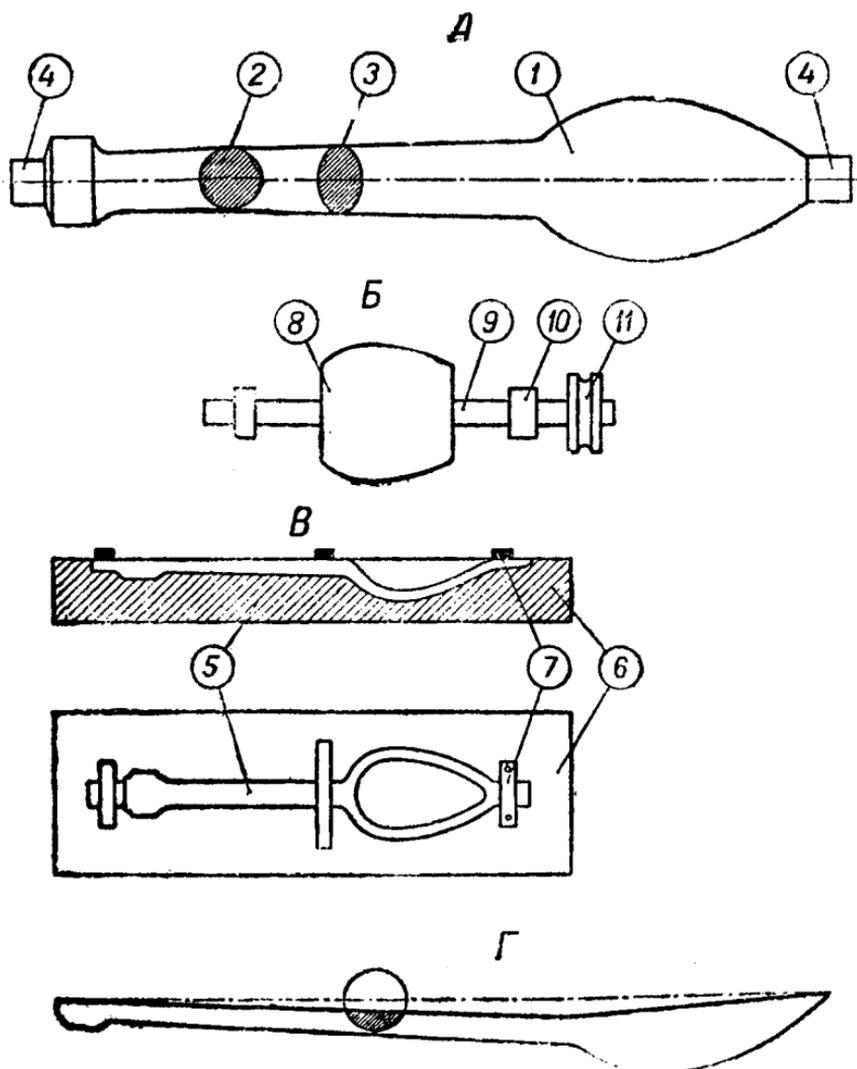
Приспособление т. Горшкова: а — болванка для двух ложек, выточенная на обыкновенном токарном станке; б — вал с фрезой и шкивом; в — доска с выемкой, куда вставляется полуболванка при обработке лунки; г — полуболванка на одну ложку.
